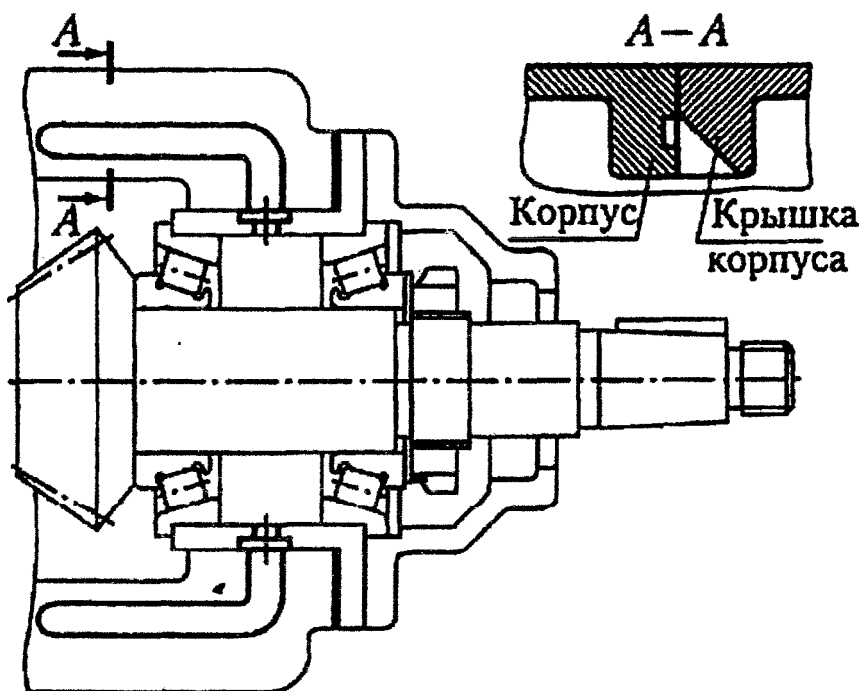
Вариант конструктивного решения облегчения смазывания подшипников вала конической шестерни [5]
